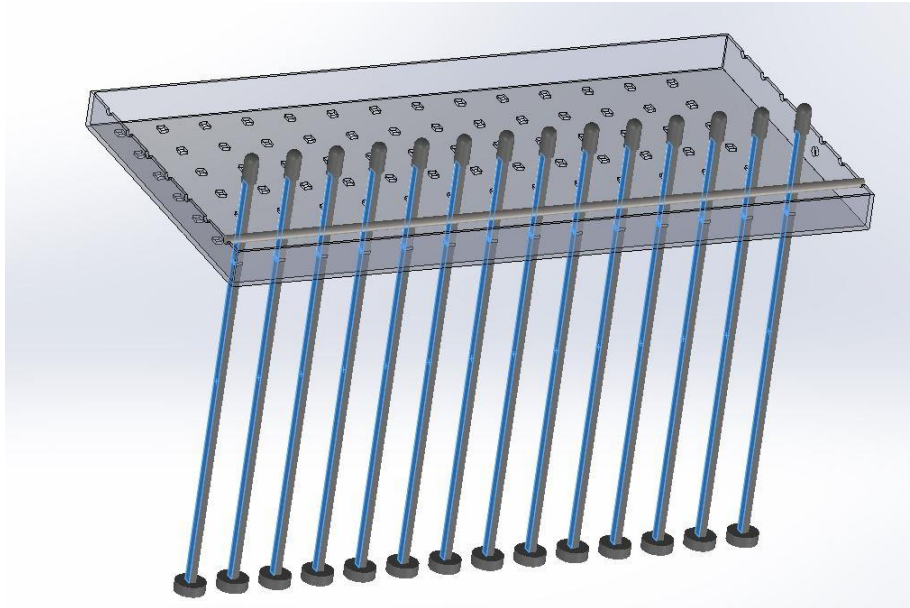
Faces onde foi aplicado o constrangimento entre atuador e base do bloco
